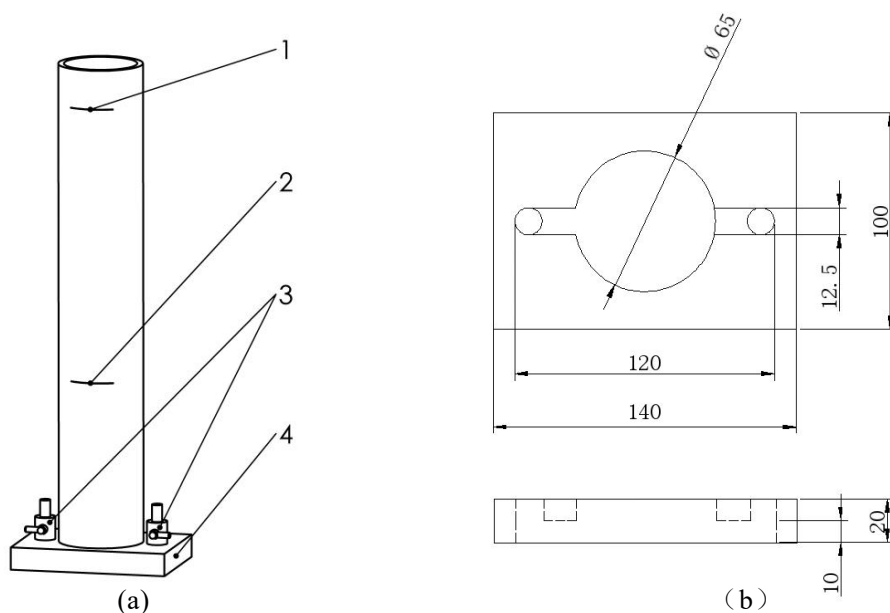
底部开口的带底座塑料量筒示意图（单位：mm）
